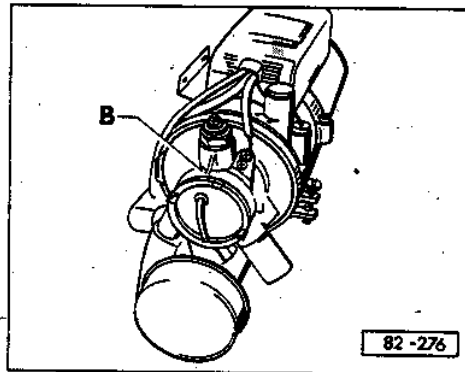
Vlies für Dieselheizgerät instand setzen
